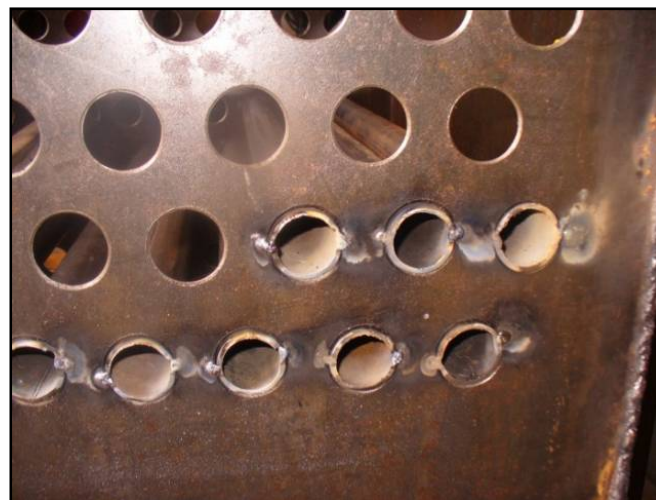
10 Intercambiador de Calor, Arreglo Soldado de Tubos
